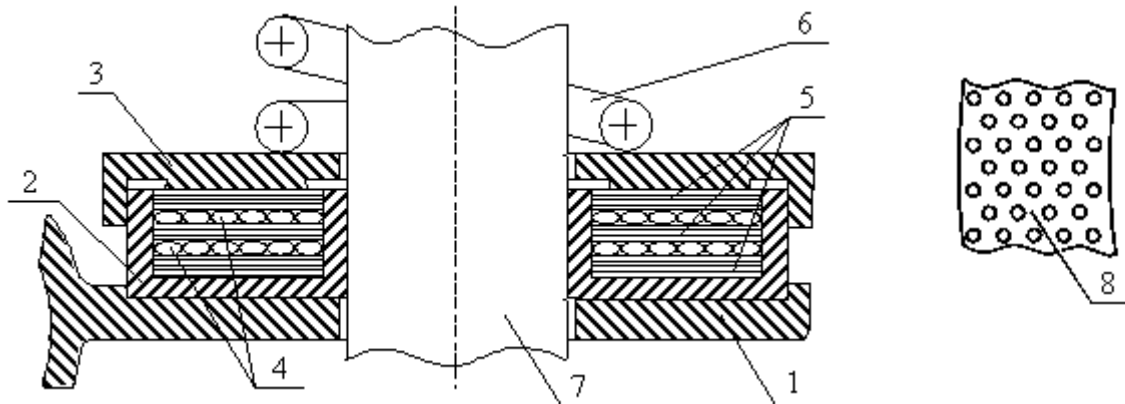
Схема пластинчатого виброизолятора: 1 – проушина буксы; 2 – корпус; 3 – верхняя крышка; 4 – тросовые пакеты квазизамкнутых колец [2]; 5 – пакеты шайб; 6 – пружина буксового подвеса; 7 – шингтон; 8 – рельеф поверхности пластин
